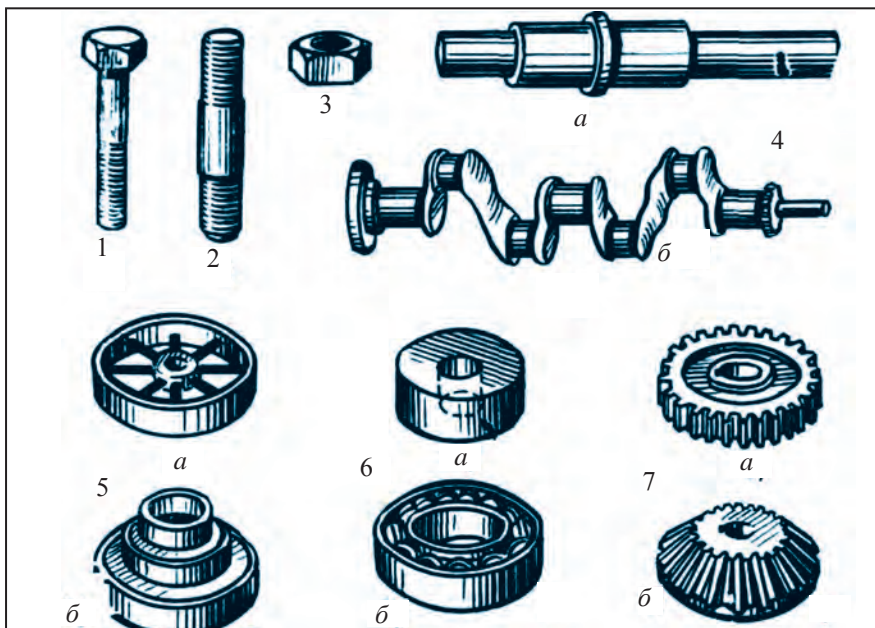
Образцы деталей машин: 1 – болт; 2 – шпилька; 3 – гайка; 4 – валы: *а*) прямые; *б*) коленчатые; 5 – шкивы: *а*) одноступенчатые, *б*) трёхступенчатые; 6 – подшипники: *а*) скользящие, *б*) катящиеся; 7 – зубчатые колёса: *а*) цилиндрические; *б*) конусовидные.
